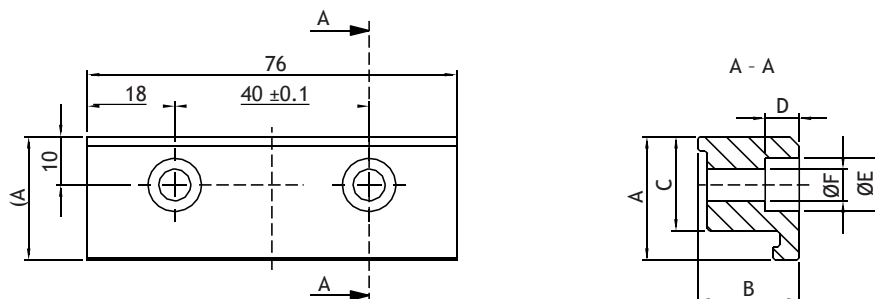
Disegno dimensionato di una staffa di fissaggio corta
